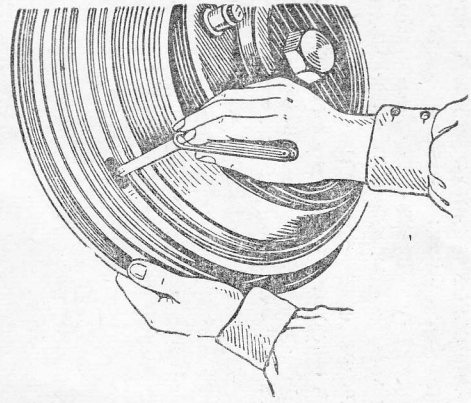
Способ замера зазора между тормозными колодками и барабаном.
